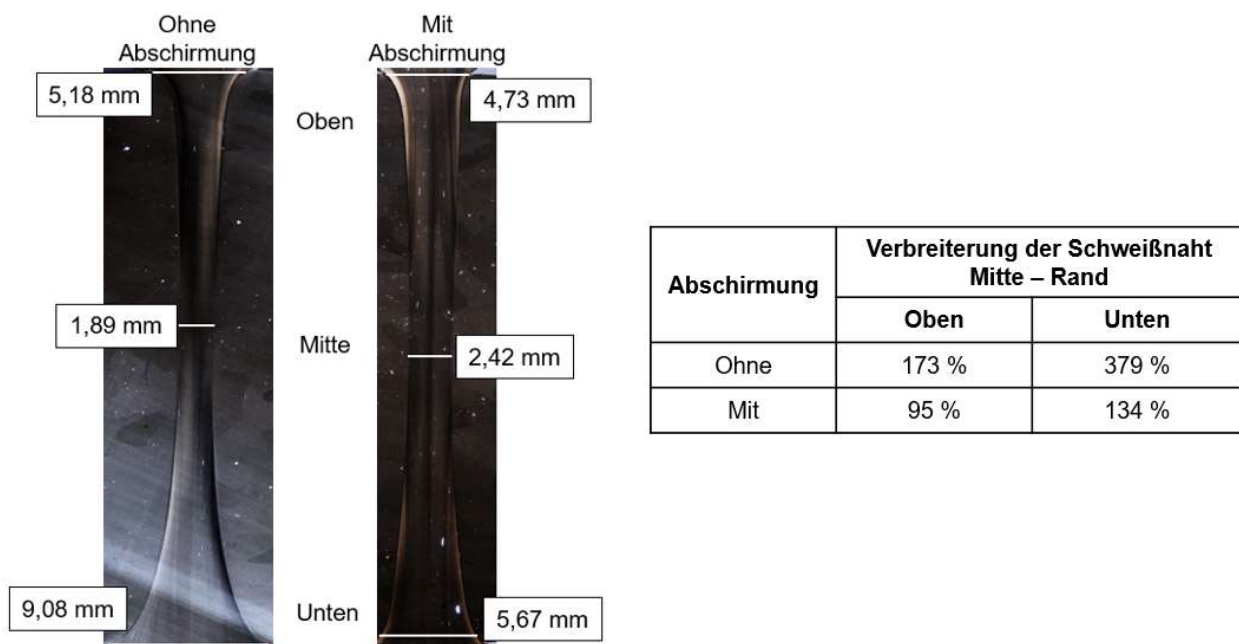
Verringerung der Schweißnahtkrümmung mittels Aluminiumabschirmung
